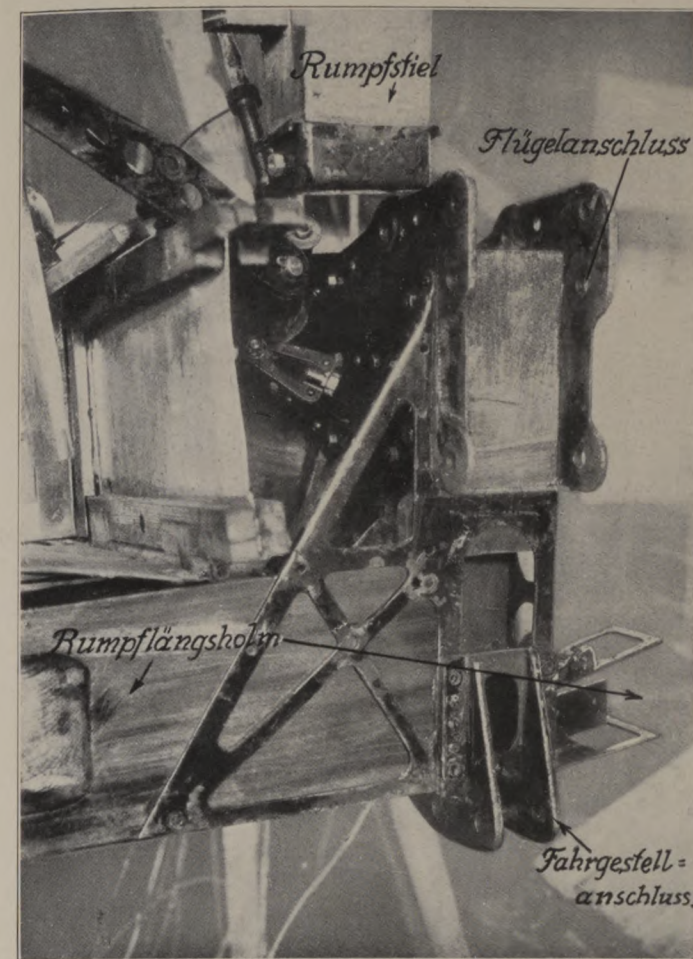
Handley-Page-G-Flugzeug. Holmbeschläge.
